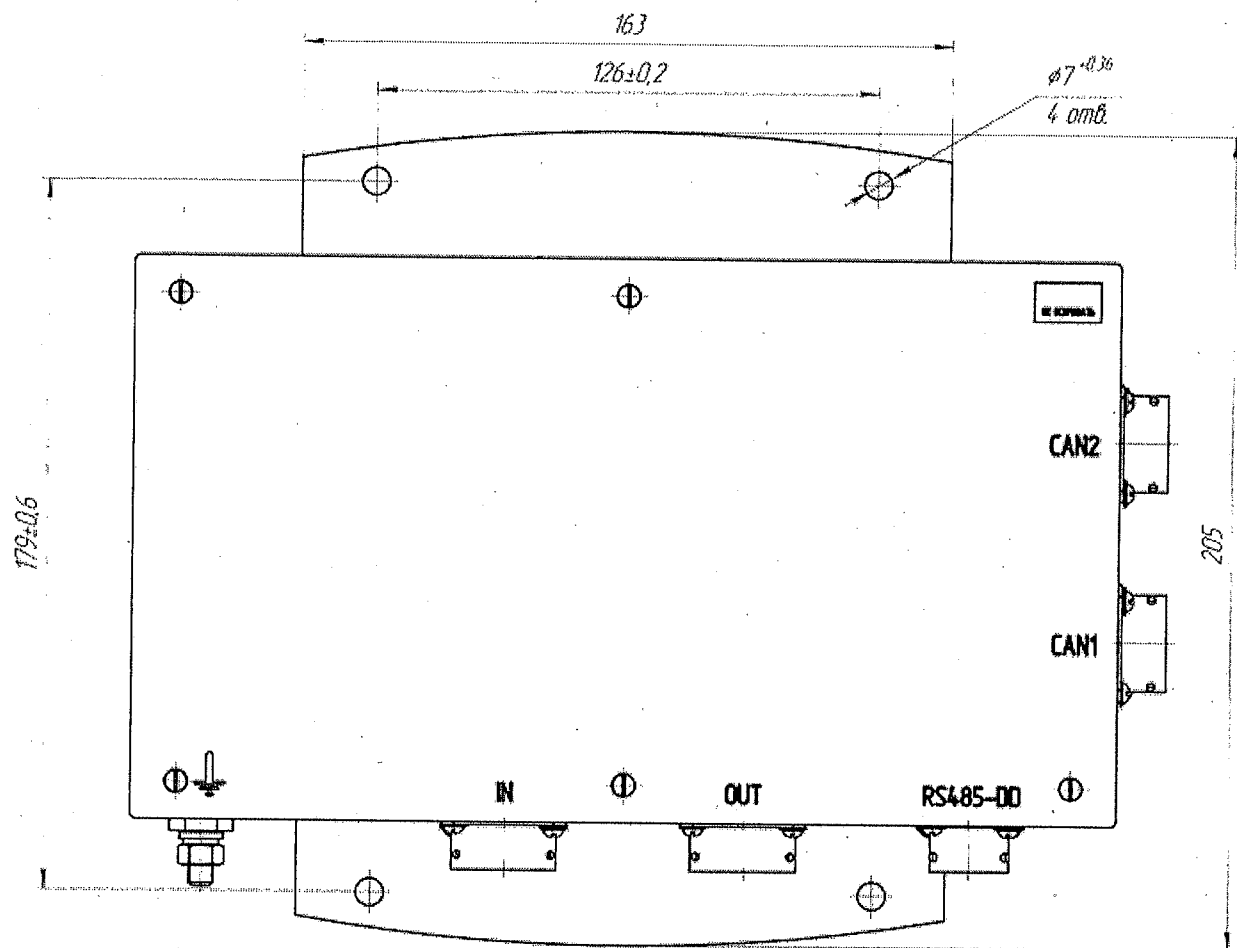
Внешний вид блока ВВД-03 36311-40-00-03
